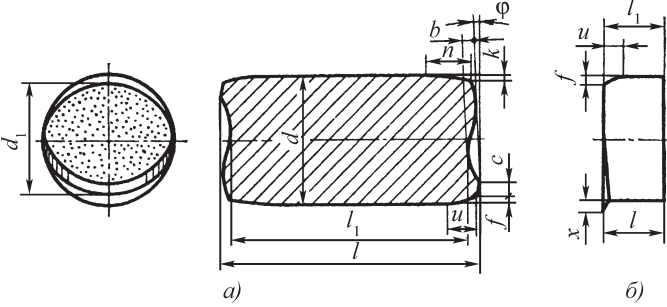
Схемы измерения заготовки, отрезанной не полностью открытой или не полностью закрытой отрезкой (а), и точной короткой заготовки (б), полученной закрытой отрезкой
